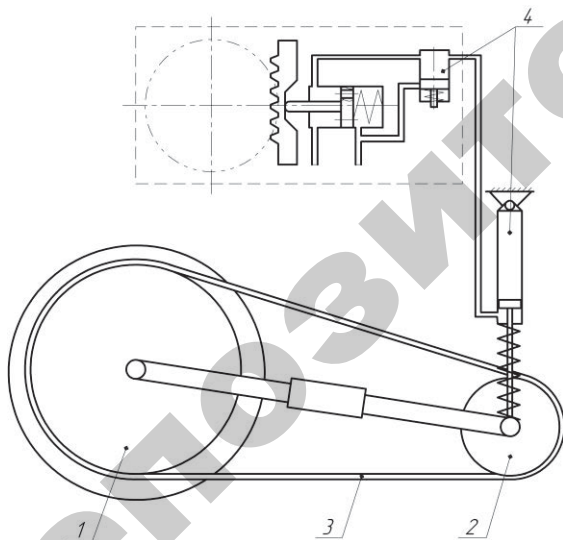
Полугусеничный ход колесного трактора: 1 – ведущее колесо; 2 – ведомое колесо; 3 – гибкий обод; 4 – гидросистема трактора
